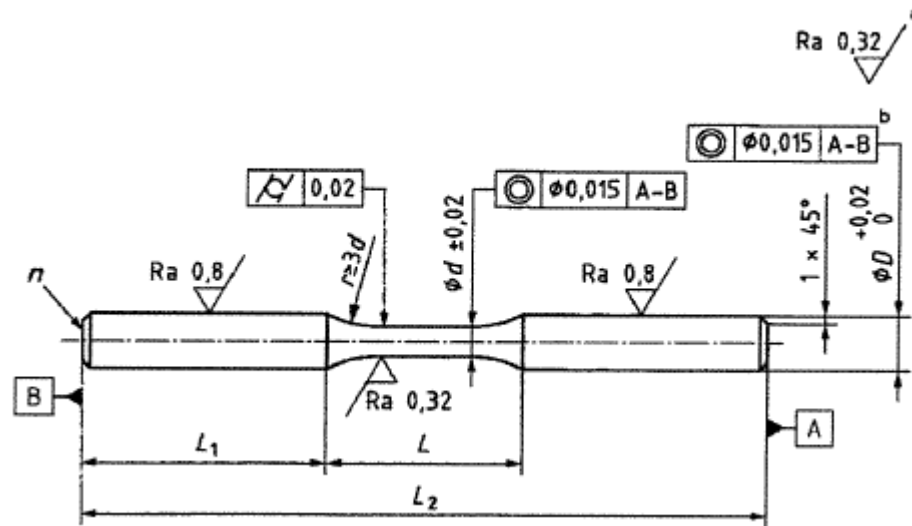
Forma y dimensiones de una probeta cilíndrica típica [12]
